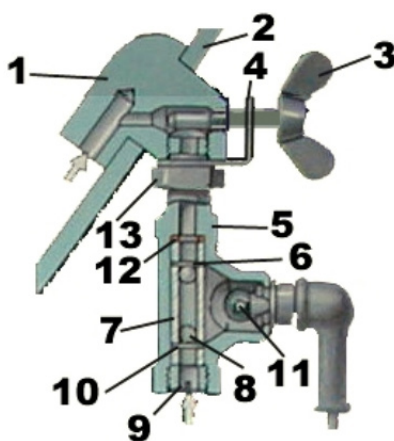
Прибор для контроля избыточного давления воздуха:
